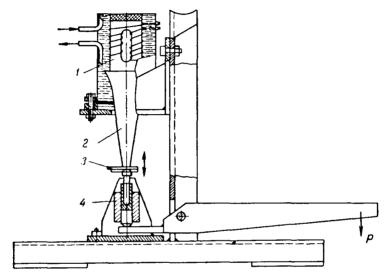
Схема машины для сварки пластмасс ультразвуком: 1—вибратор; 2—волновод; 3—свариваемый материал; 4—иастроенный отражатель.
